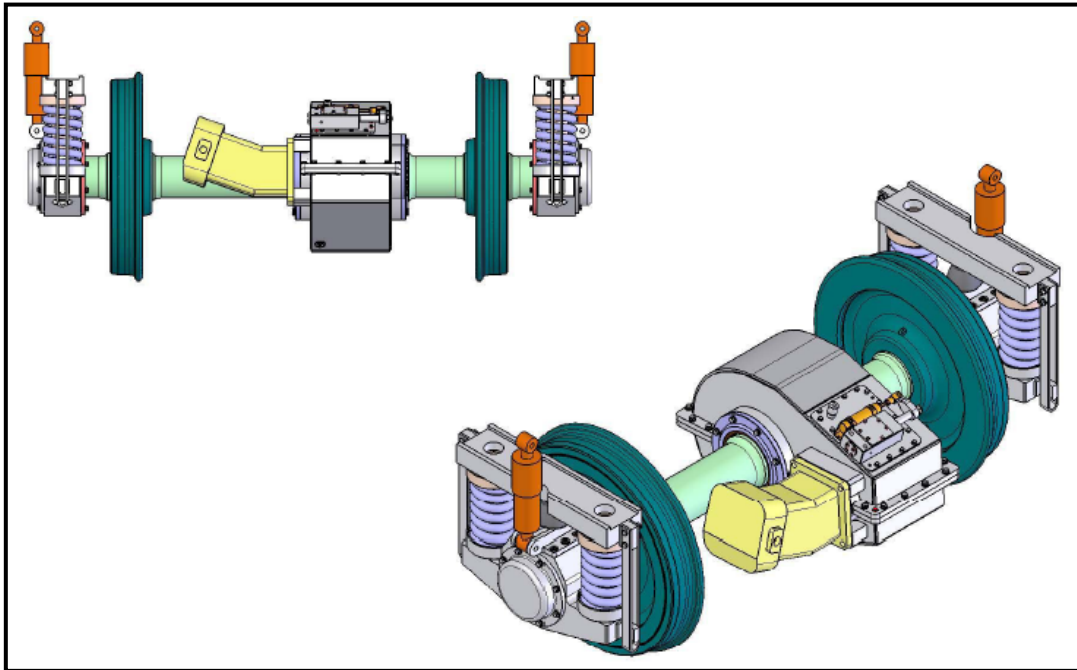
Diseño final conjunto del sistema de rodadura dresina
